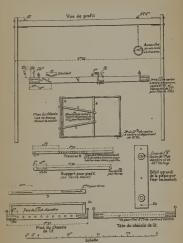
Cadre-Hamac de Sinclair. — Détail et dimensions du chassis et du cadre. Voir é-galement fig.5 et 5 bis (D'après Sinclair).
